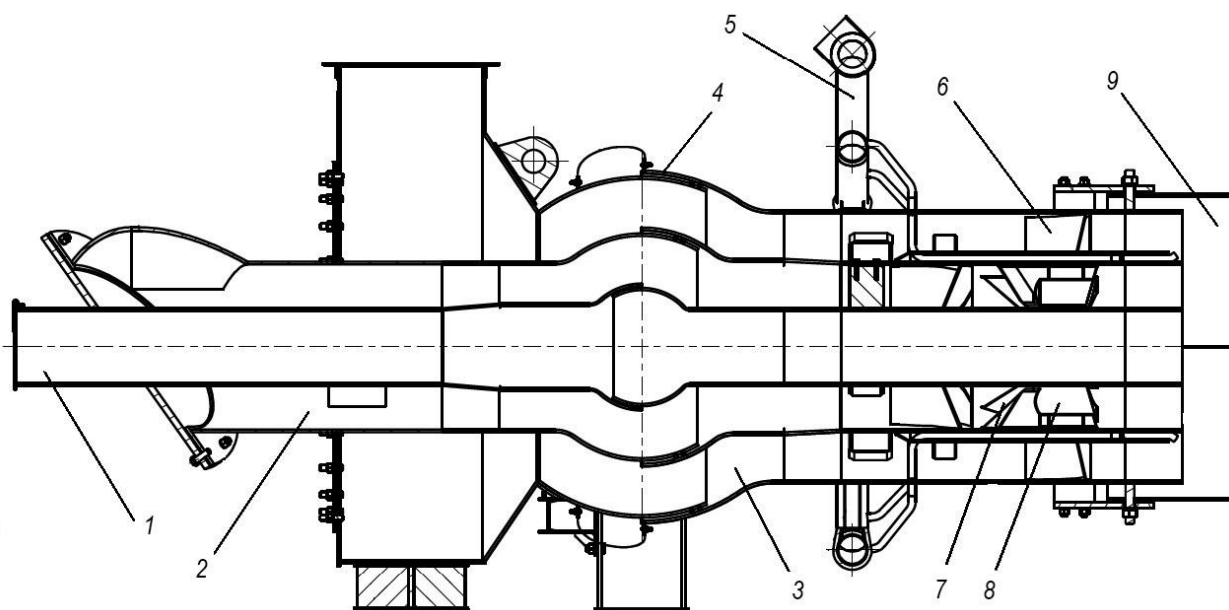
Вид горелки сбоку в разрезе (1 – центральный канал (место размещения запального устройства и мазутной форсунки); 2, 3 – каналы подачи аэросмеси и вторичного воздуха; 4 – узел сопряжения статичной и поворотной частей горелки; 5 – газовый коллектор; 6, 7 – аксиальный лопаточный аппарат каналов вторичного воздуха и аэросмеси; 8 – рассекатели потока аэросмеси; 9 – выходная насадка для горизонтального поворота)
